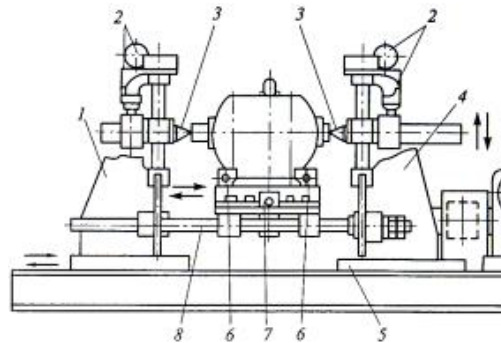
Стенд для розбирання електродвигуна: 1 – рухлива стійка; 2 – електропривод; 3 – пінолі; 4 – нерухома стійка 5 – поворотний стіл; 6 – затискачі; 7 – стіл; 8 – напрямні
